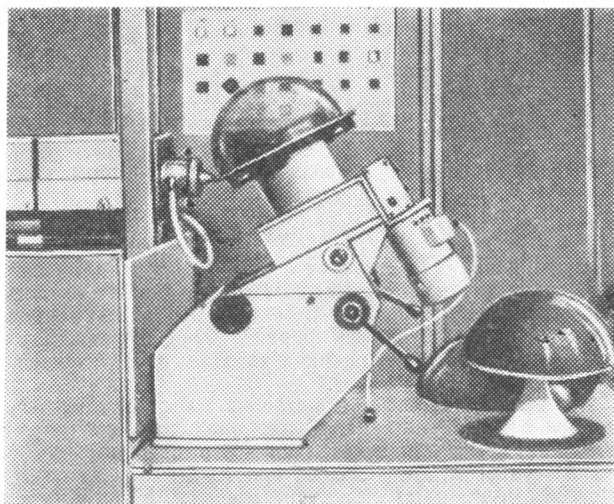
CO_2 -лазер в комбинации с простым поворотным устройством для лазерной резки полиметилметакрилата при изготовлении настольных ламп
